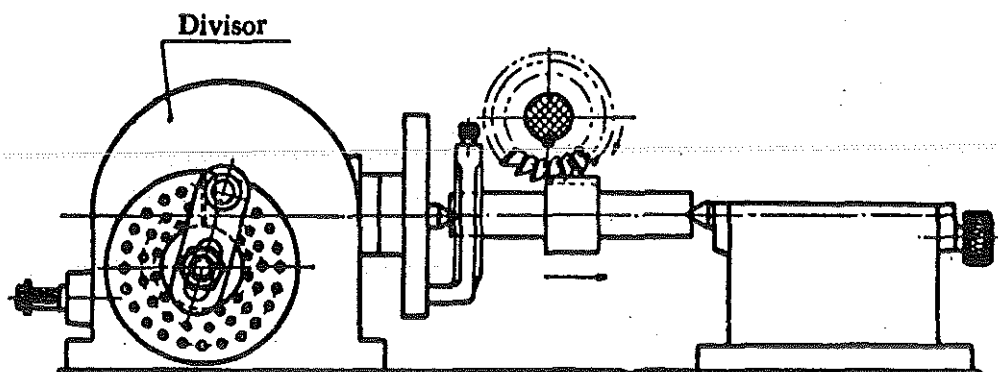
Corte de uma engrenagem por uma fresa de forma.
